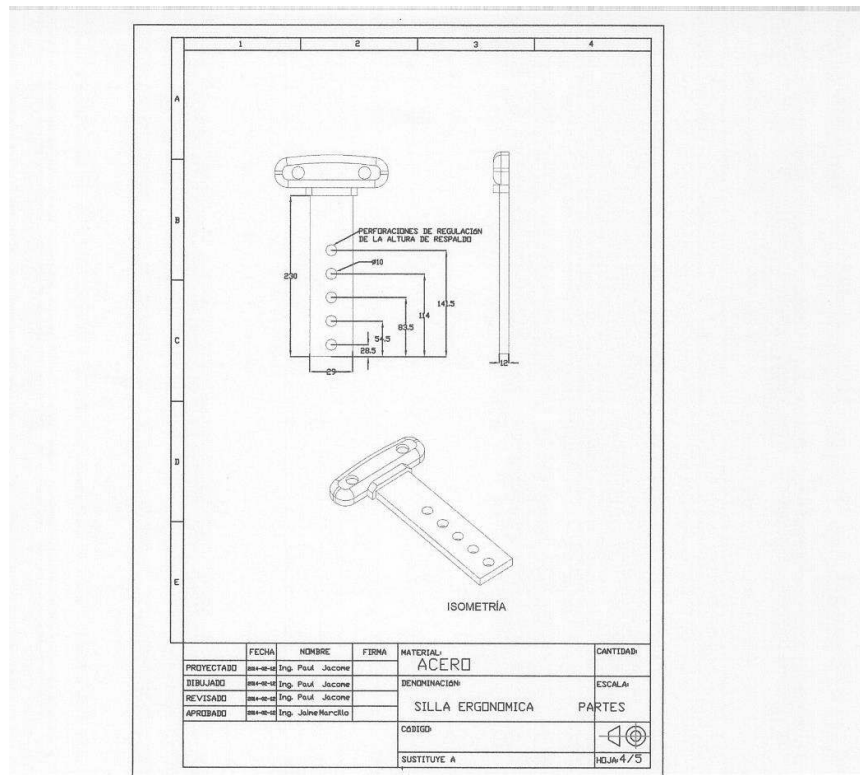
Plano de construcción soporte regulable para respaldo
